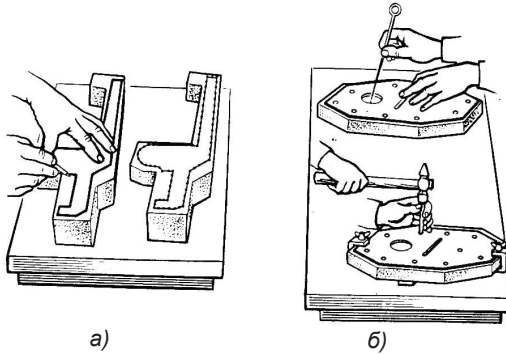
Разметка по шаблону: а) работа чертилкой и размеченная заготовка, б) работа чертилкой и накернивание.
